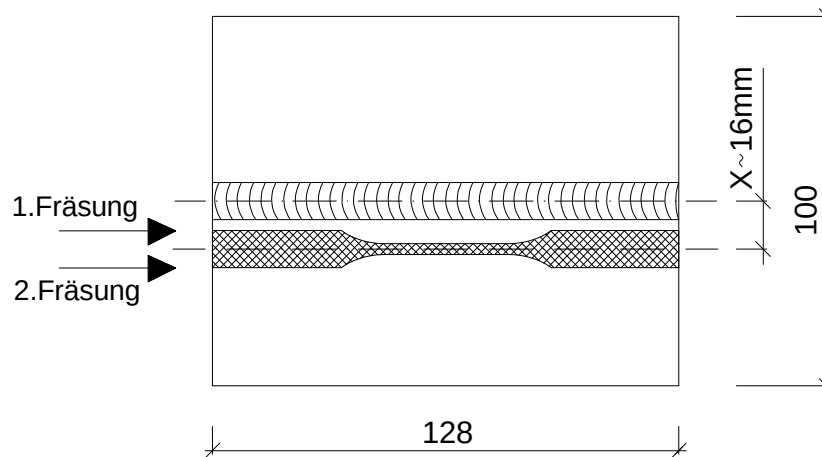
Prinzipskizze der Zugprobenentnahme an geschweißten Blechen
